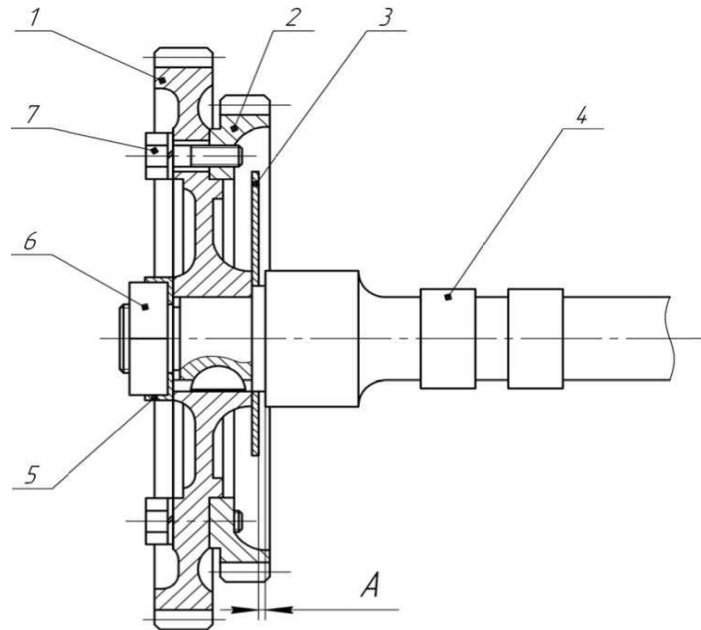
Розподільний вал 238-1006010-B5
